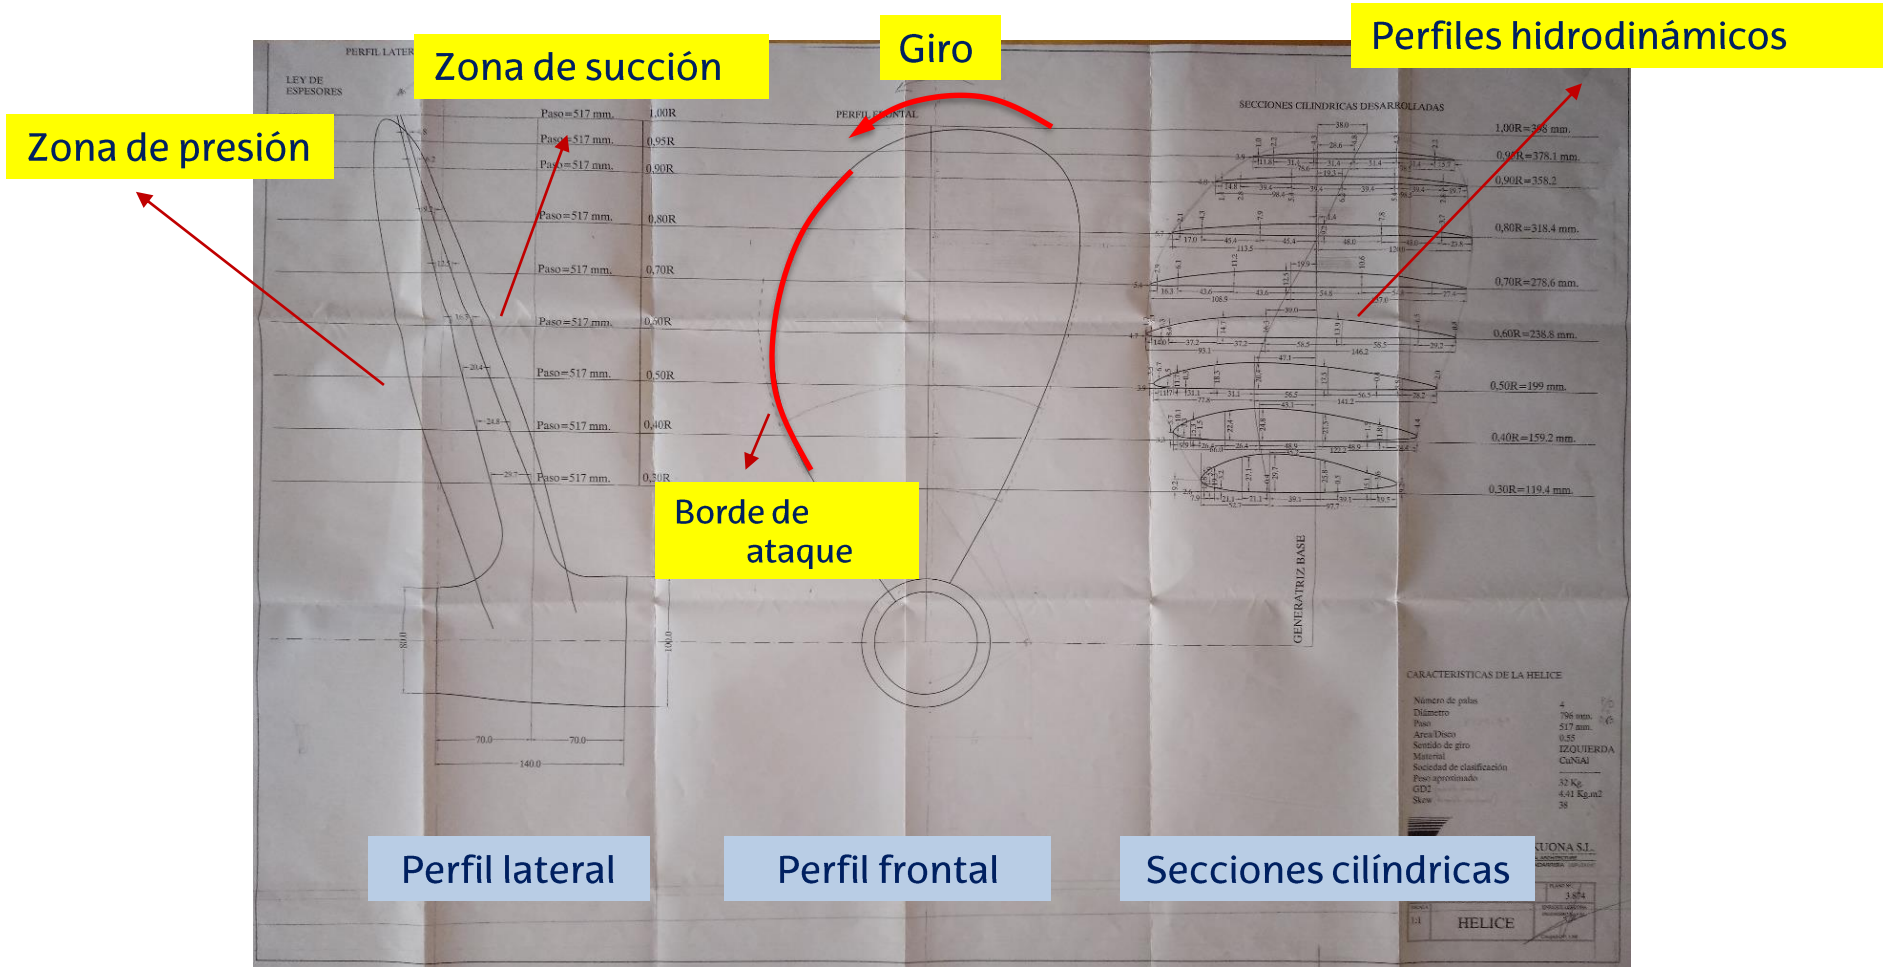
Plano constructivo de la hélice del Saltillo [1]
